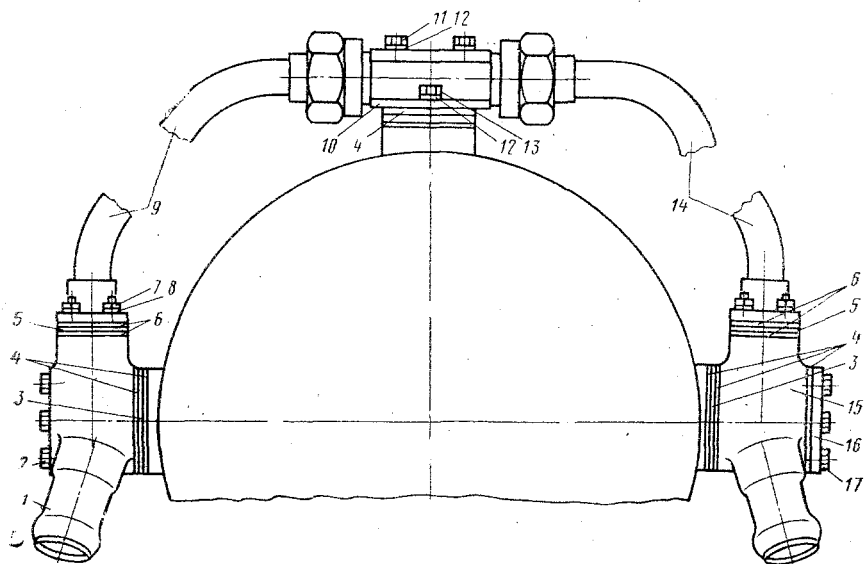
Схема установки дополнительного патрубка сброса воздуха из полостей № 15 II опоры (вид спереди):
